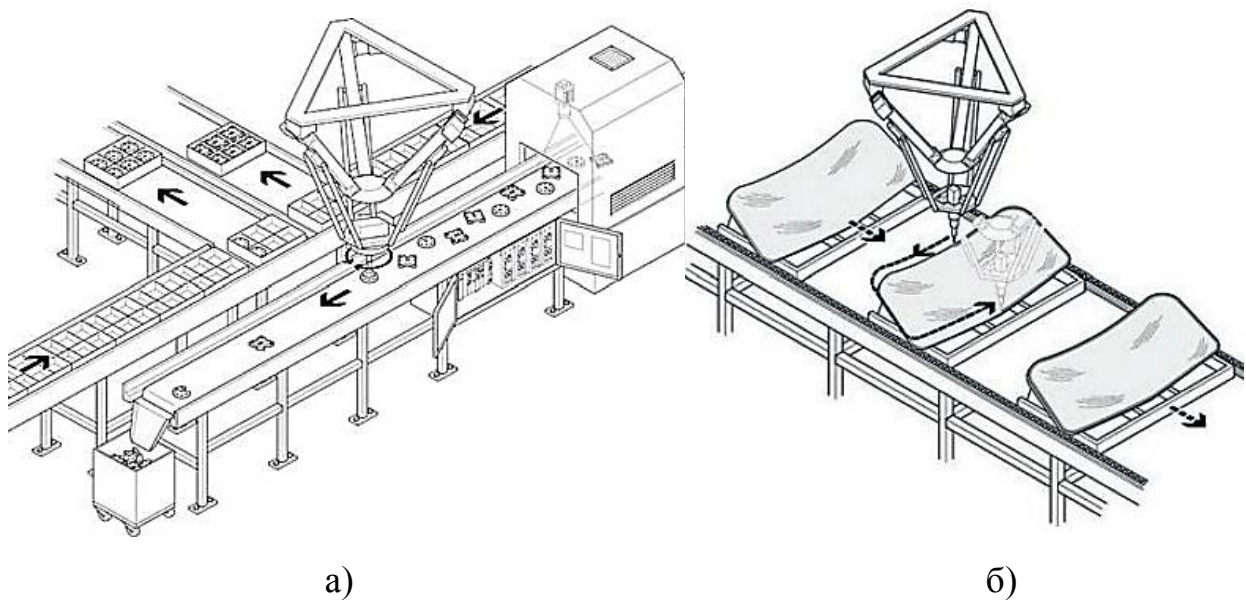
Дельта-манипуляторы в технологическом процессе: а) сортировка, отбраковка и упаковка готовой продукции; б) процесс нанесения клея по контуру упаковки
